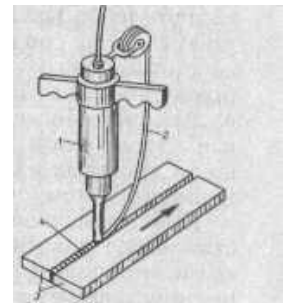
Схема сварки с дополнительным присадочным материалом: 1 – преобразователь с волноводом-инструментом; 2 – присадочный материал; 3 – свариваемое изделие; 4 – сварной шов
